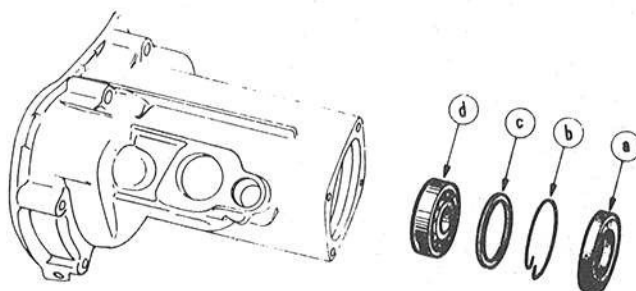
Einbau des hinteren Kugellagers mit dem Simmerring
